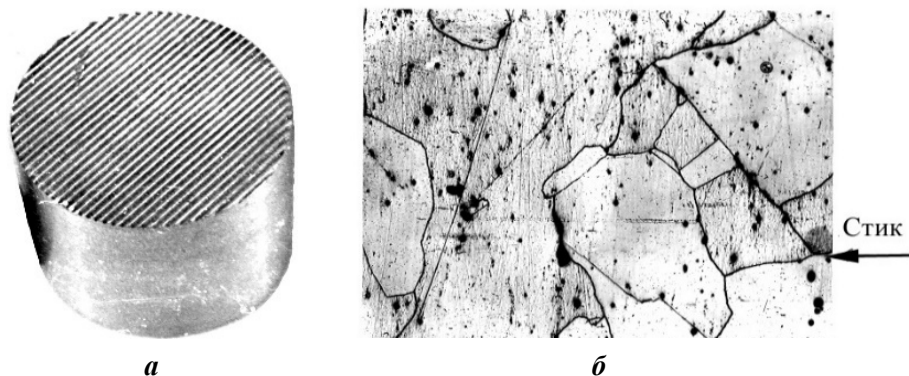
Загальний вигляд зразка, підготовленого до зварювання (а), та мікроструктура з'єднання (б);  $\times 50$
